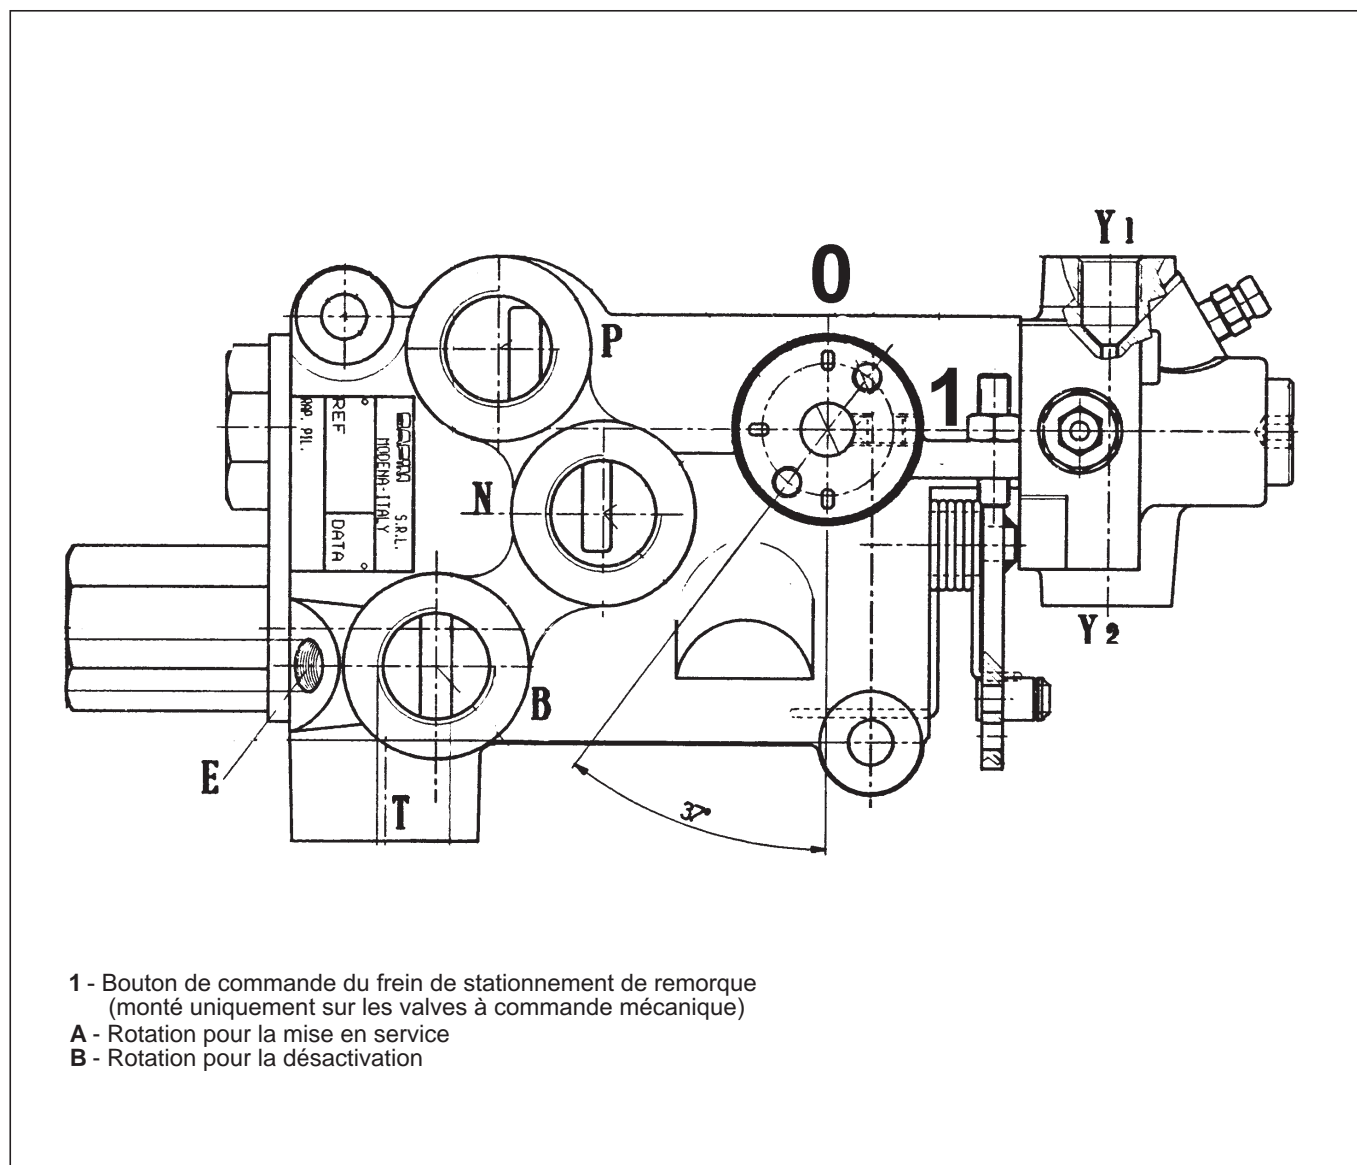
Distributeur pour le freinage hydraulique de remorque.
